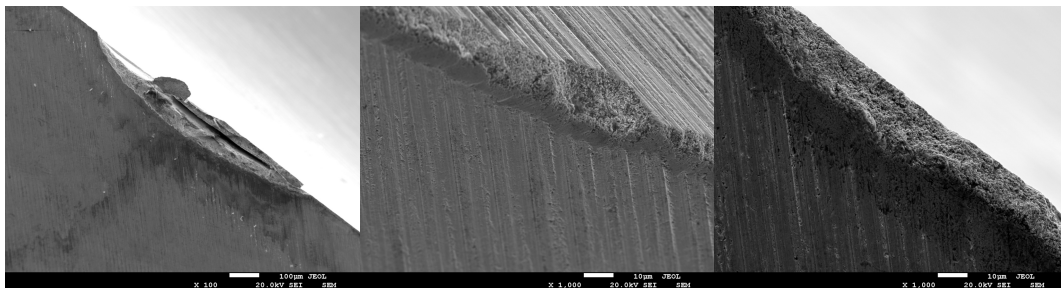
Дефекты режущей кромки цельной твердосплавной концевой фрезы полученные на стадии изготовления (до эксплуатации).
